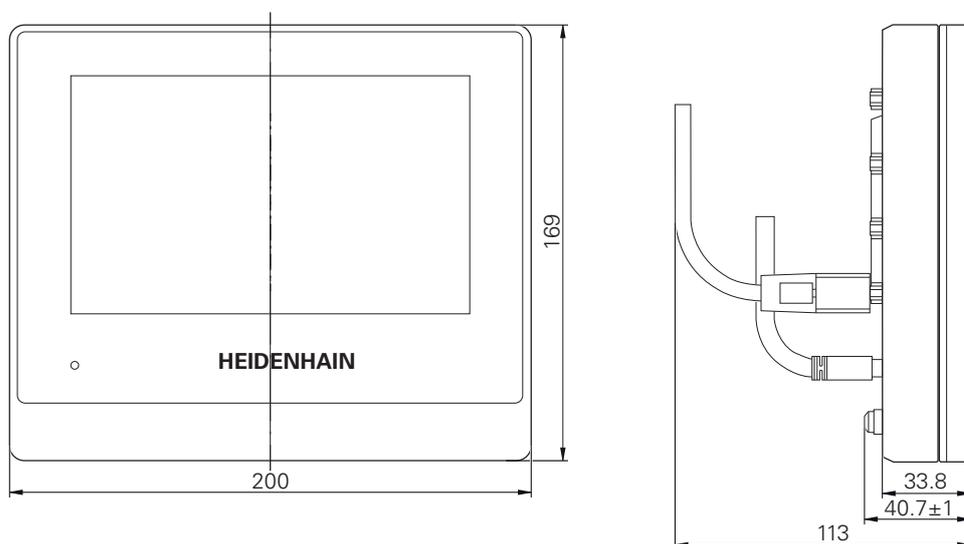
Размеры корпуса устройств с ID 1089178-xx
